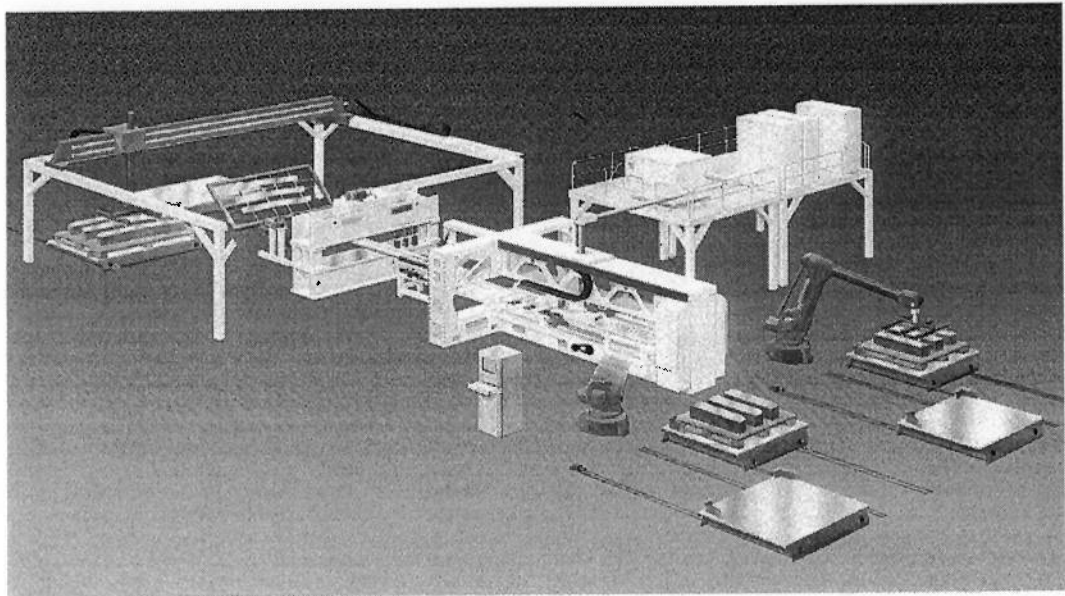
Sistema de Soldagem Soulas – Lay-out do equipamento de solda a laser para fabricação dos blanks soldados [Pincinini99].
